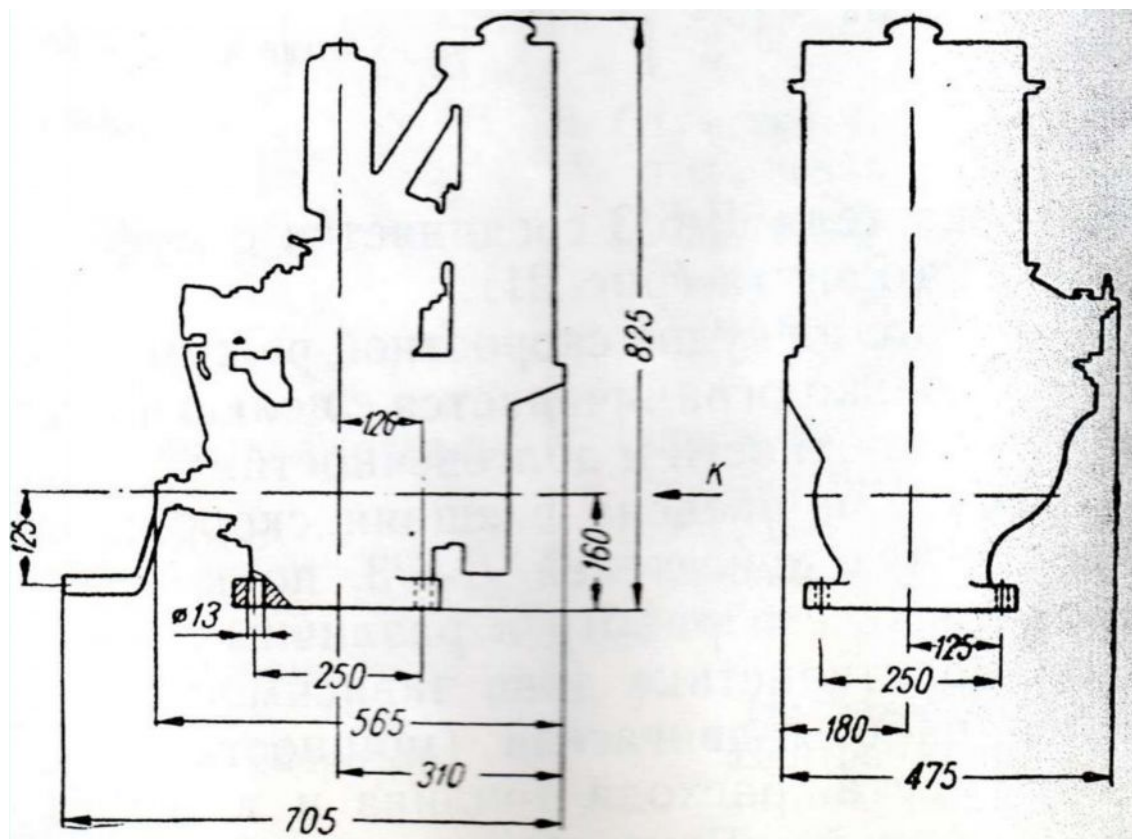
Основные габаритные размеры двигателя Л-6/3.
